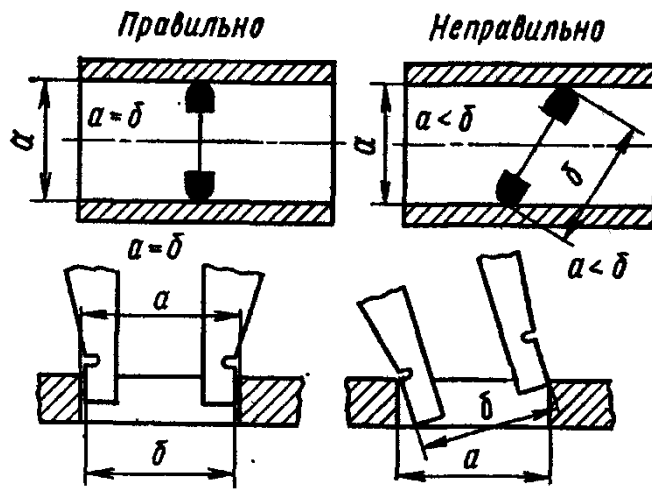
Установка штангенциркуля при измерении внутренних поверхностей
